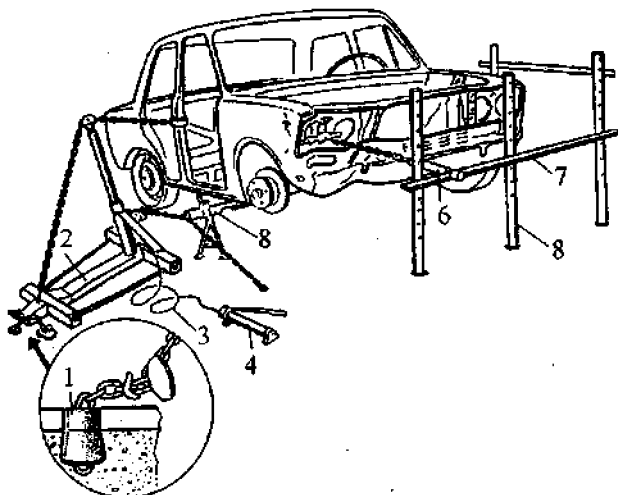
Стенд BC-132 с анкерными устройствами
